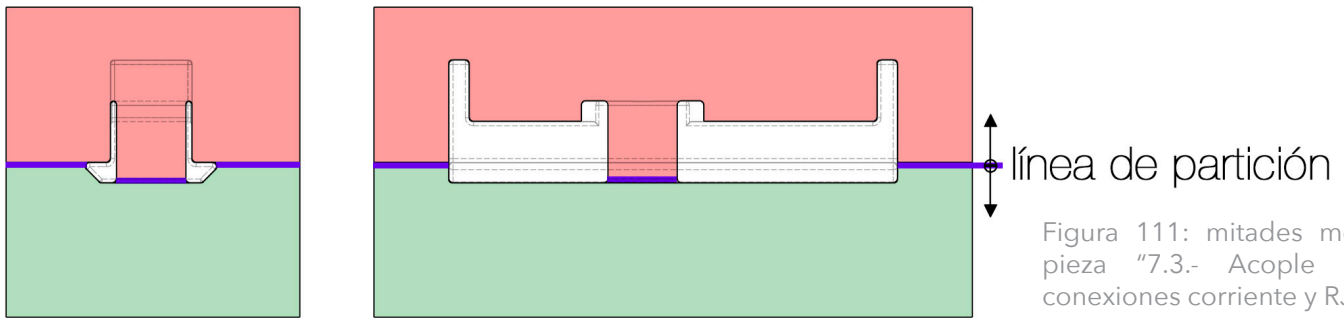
mitades molde pieza "7.3.- Acople guía conexiones corriente y RJ45"
